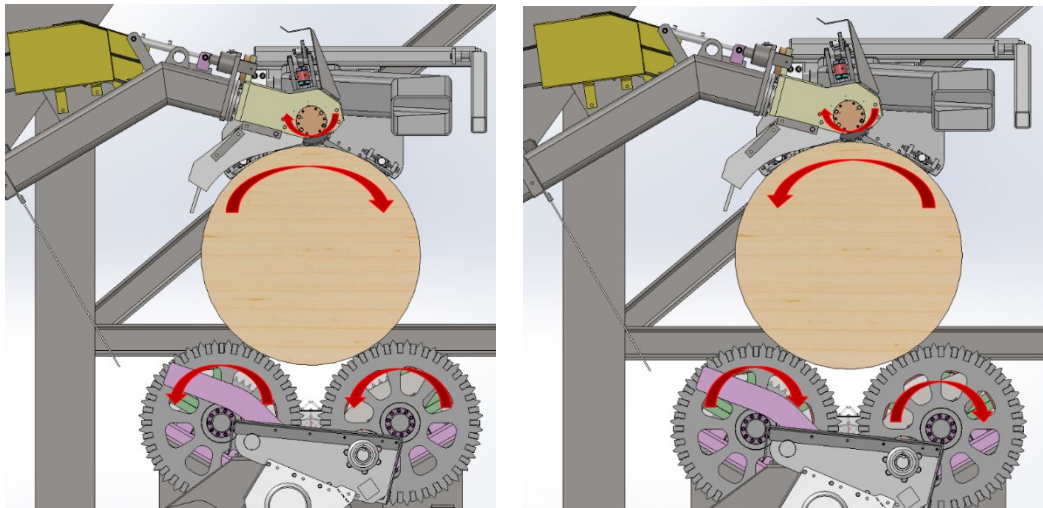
Gegenlauf und Gleichlauf (Quelle: Baljier & Zembrod GmbH & Co. KG)
